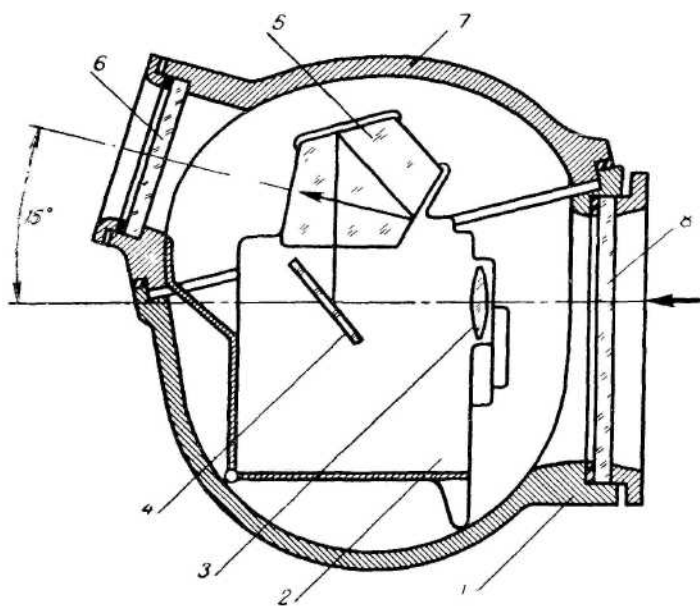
Подводный бокс в разрезе: 1 — корпус бокса; 2 — фотоаппарат «Спутник»; 3 — объектив видоискателя; 4 — зеркало видоискателя; 5 — пента - призма видоискателя; 6 — иллюминатор видоискателя; 7 — крышка бокса; 8 — иллюминатор
